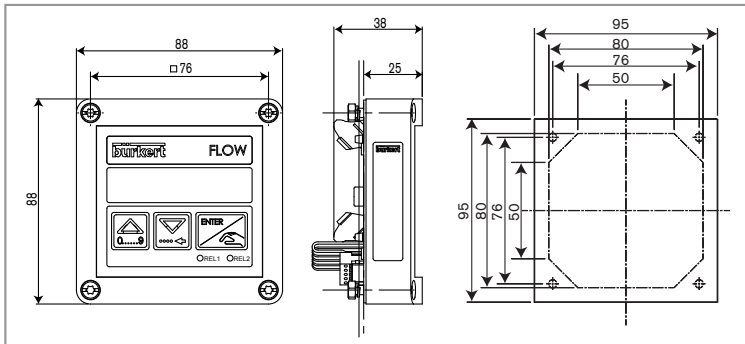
Dimensions du transmetteur en version encastrable et plan de découpe de la façade du coffret électrique
